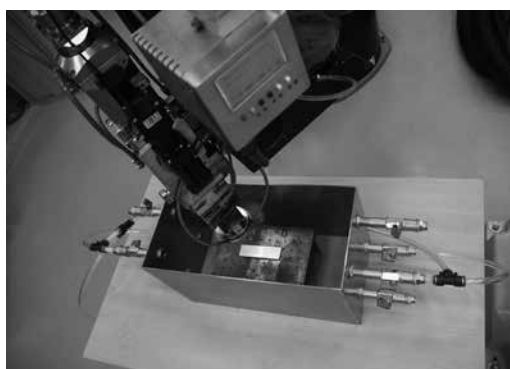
Экспериментальная установка для лазерной порошковой наплавки
